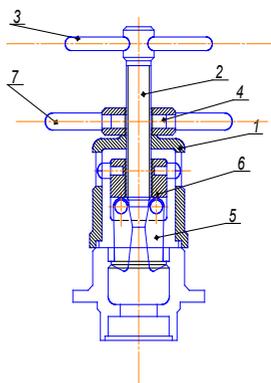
Съемник винтовой для выпрессовки обойм подшипников с помощью захватов
